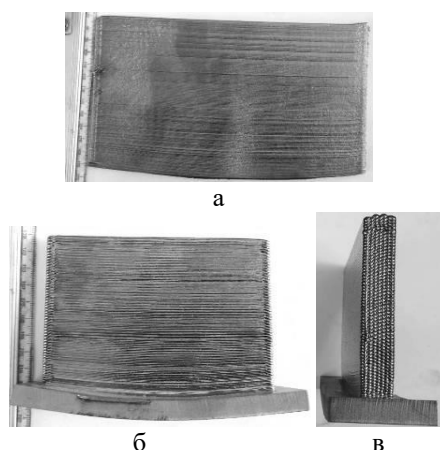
Заготовки полученные методом лазерно-порошковой наплавки:
